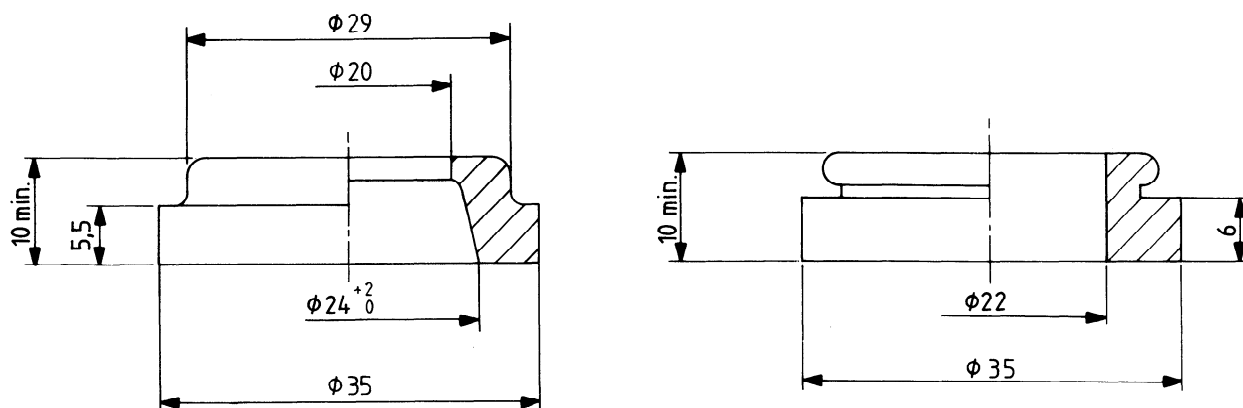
Exemple de joints d'étanchéité souples pour les raccords d'amenée d'eau
